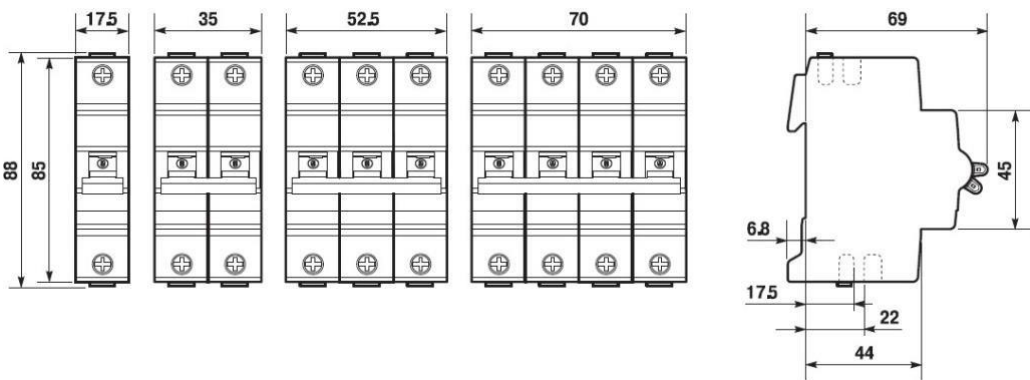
Габаритные, установочные и присоединительные размеры АВ серий S200 и SH200, мм.
